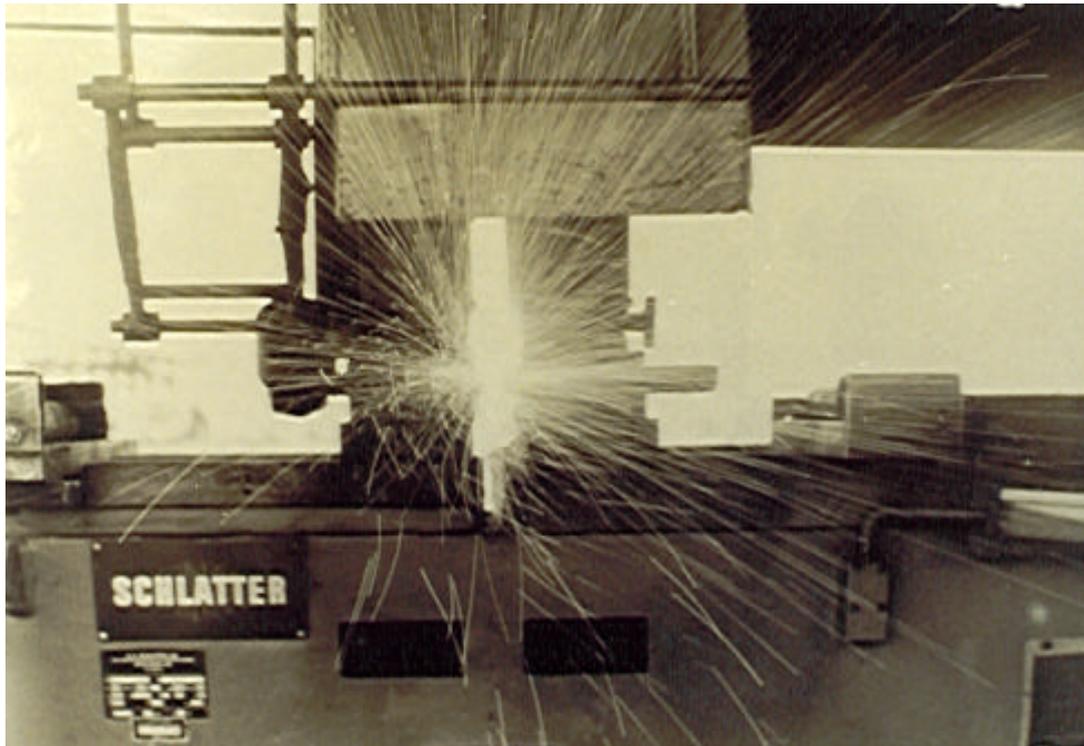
Solda topo , utilizada inicialmente em Ilha Solteira
